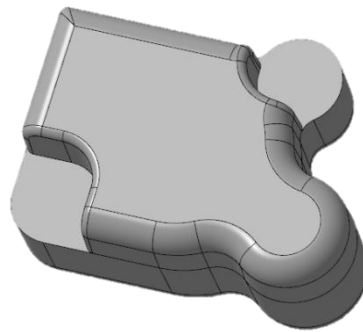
3Д модель заготовки деталі «заглушка»
